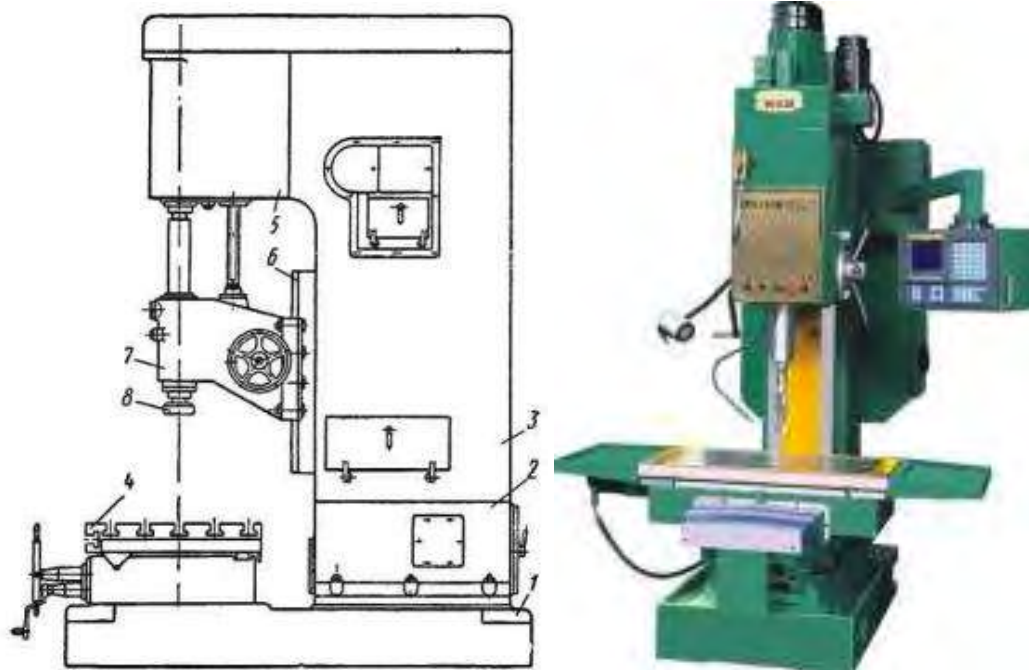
Компоновка и общий вид алмазно-расточного станка
